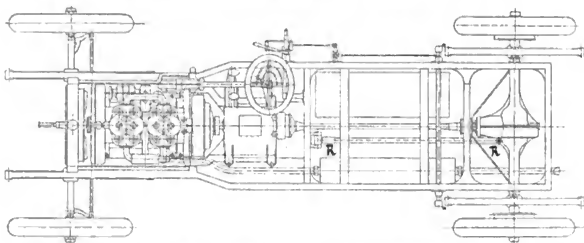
Vierzylinder-Cardanautomobil mit 2 Cardangelenken gebaut, von der N. A. G.
